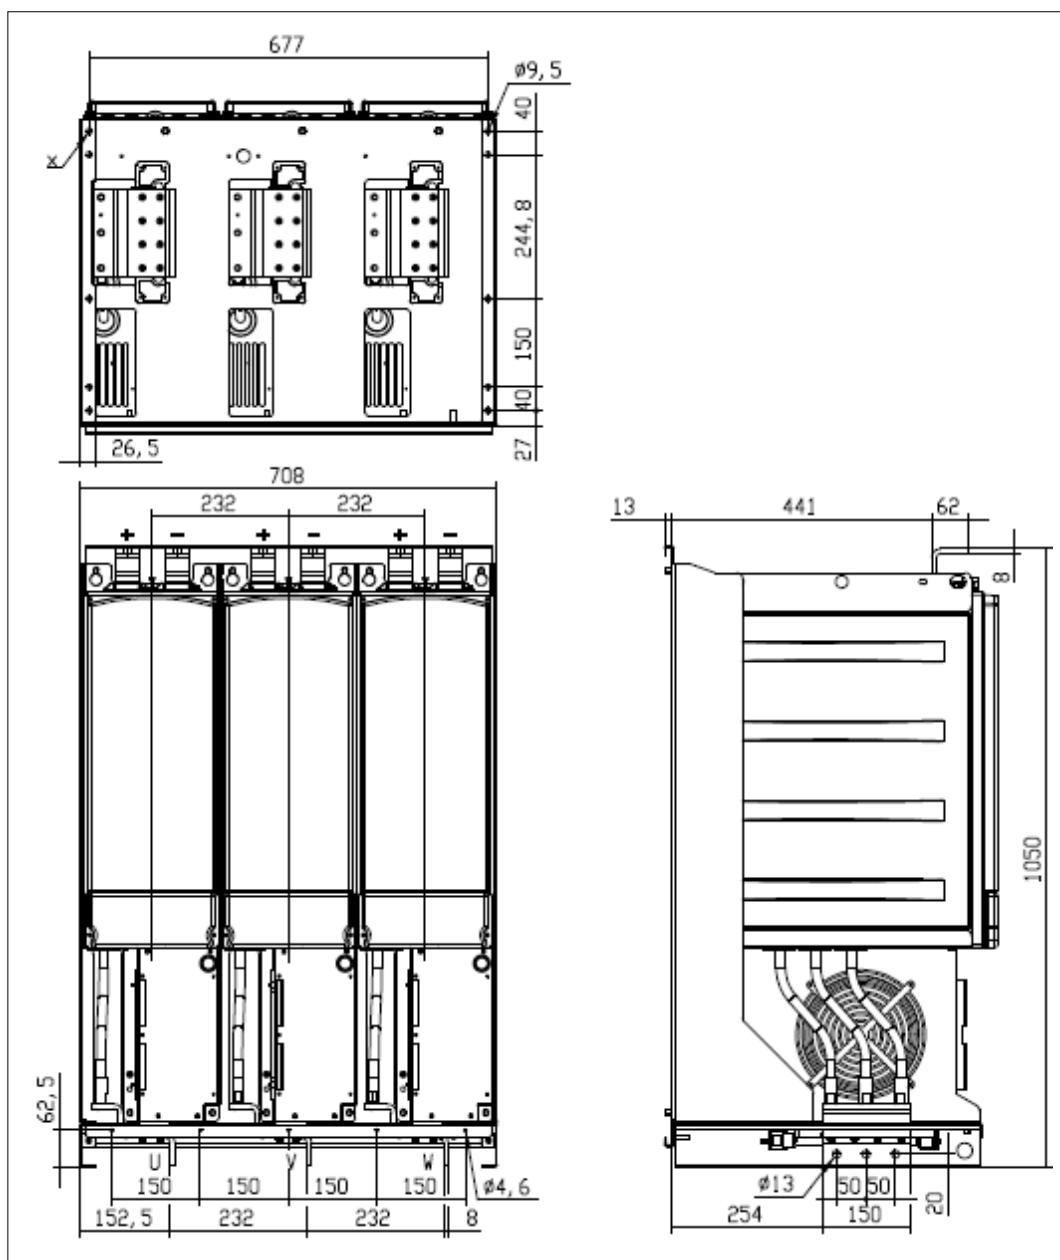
Габариты инвертора VACON® NXI, типоразмер FI13 (вид спереди).
